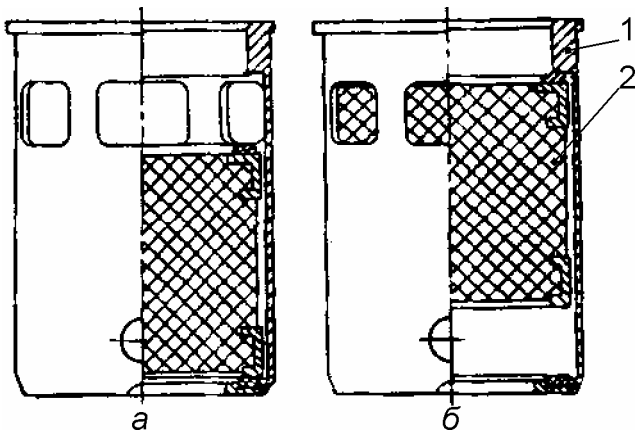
Поплавцевий дренажний клапан без важеля (МиГ-29): а — відкритий; б — закритий; 1 — корпус; 2 — поплавець
